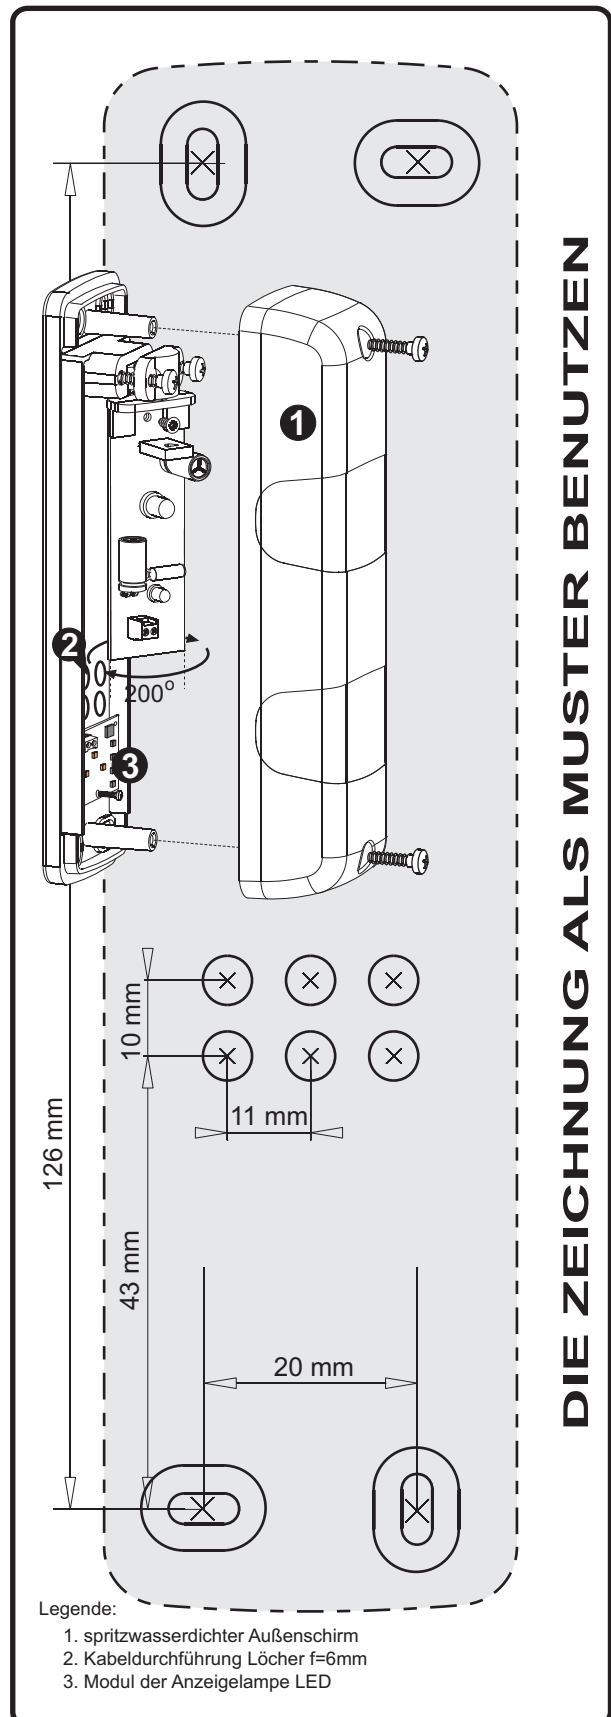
Das Bohrlochbild für Montage im Maßstab 1:1 mit Zusammenstellungszeichnung.
